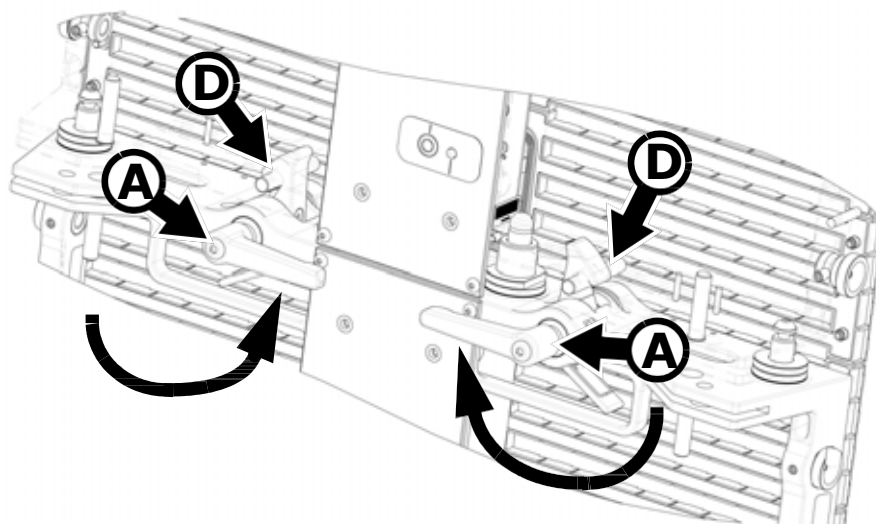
Повернуть блокирующие рукоятки, чтобы заблокировать крюки на штырях блокировки (вид в разрезе)
